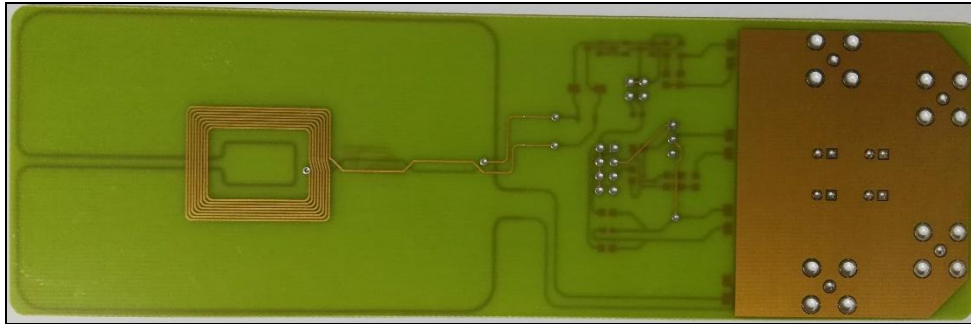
PCB PICC de Referencia N° 4 – Capa BOTTOM
